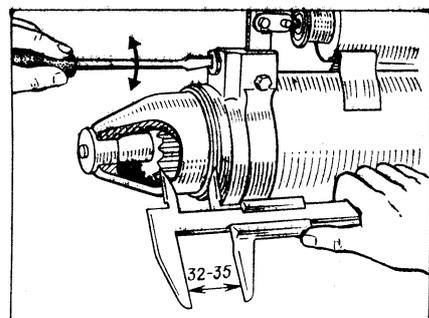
Проверка и регулировка расстояния между торцом шестерни привода и фланцем стартера СТ-117
